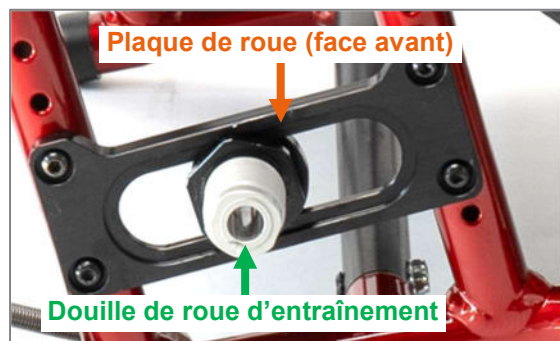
Plaque de roue pour le réglage de la hauteur d'assise à l'arrière (vue du côté extérieur du produit, roue d'entraînement enlevée)
